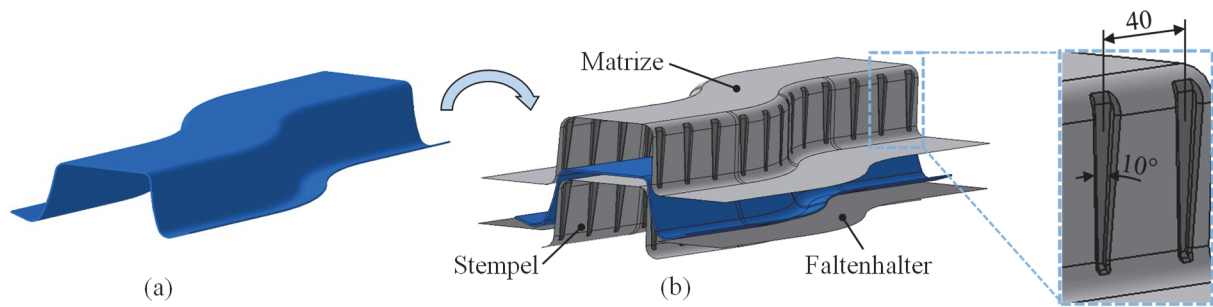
Nachformen der Bauteilzarge nach innen; (a) Bauteil nach der ersten Umformstufe, (b) Werkzeugflächen für das Nachformen; Werkstoff DP 980, $s_0=0,97$ mm
